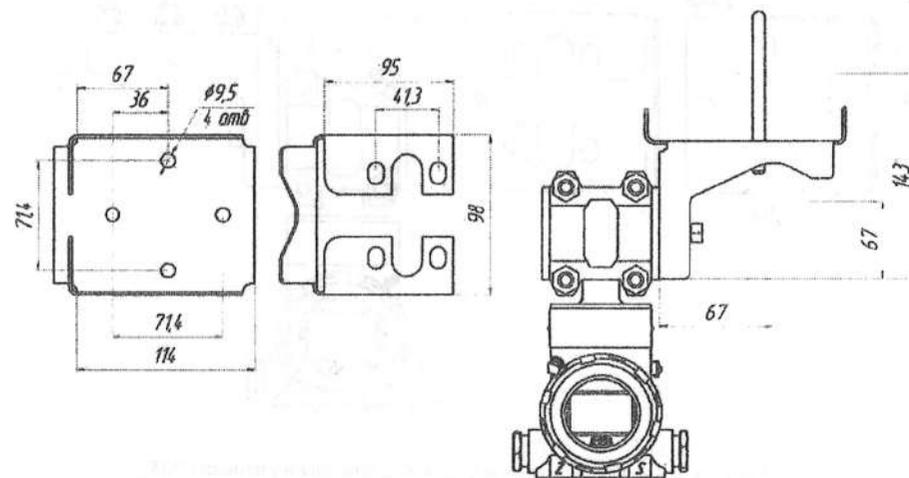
Угловой кронштейн для крепления на трубе (B04), габаритные и присоединительные размеры
